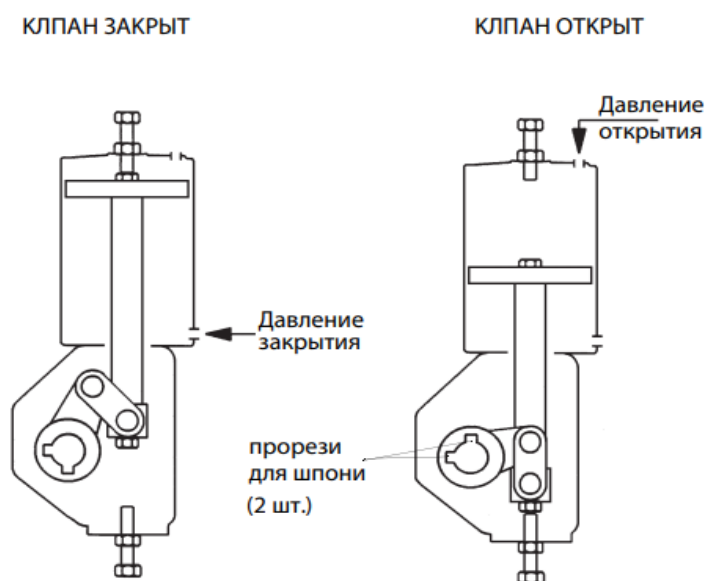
Пневматический исполнительный механизм Neles B1C двухстороннего действия
